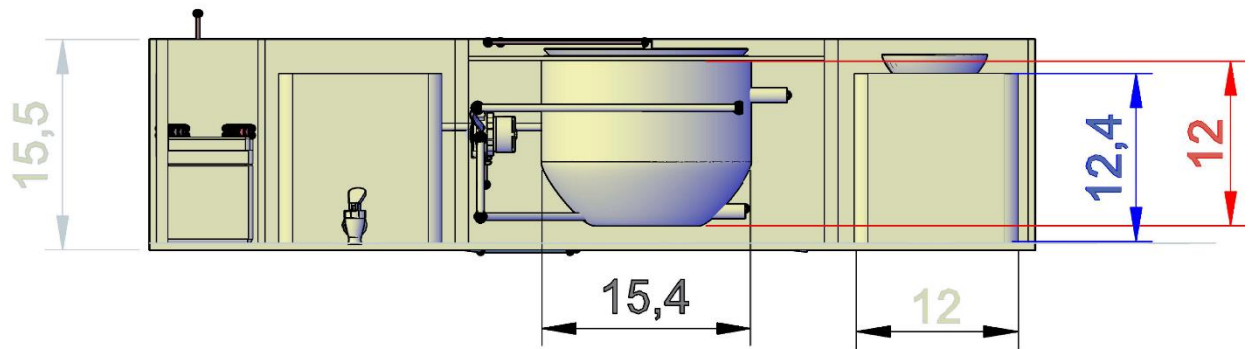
Dimensiones dispositivo de desinfección electroquímica vista frontal
